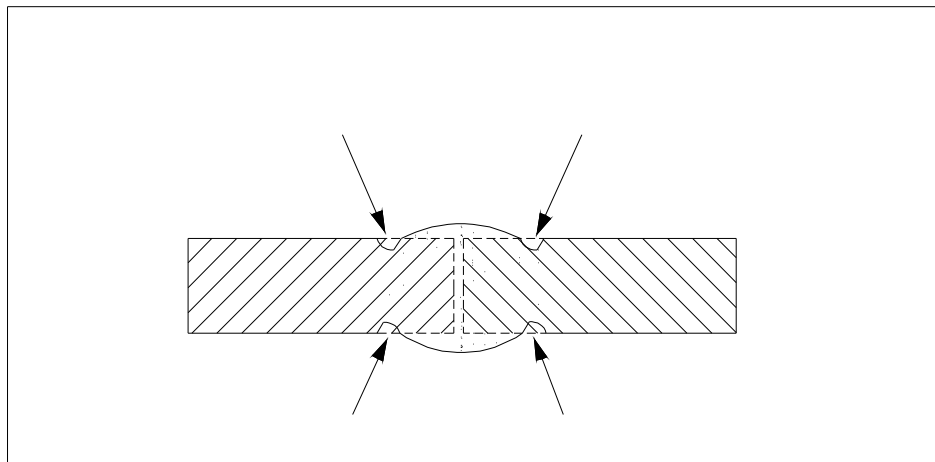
Socavamiento en soldadura a tope (SOLDADURA, APLICACIONES Y PRACTICAS, Henry Horwitz, P.E.1997, capítulo 22, Pág. 688).
